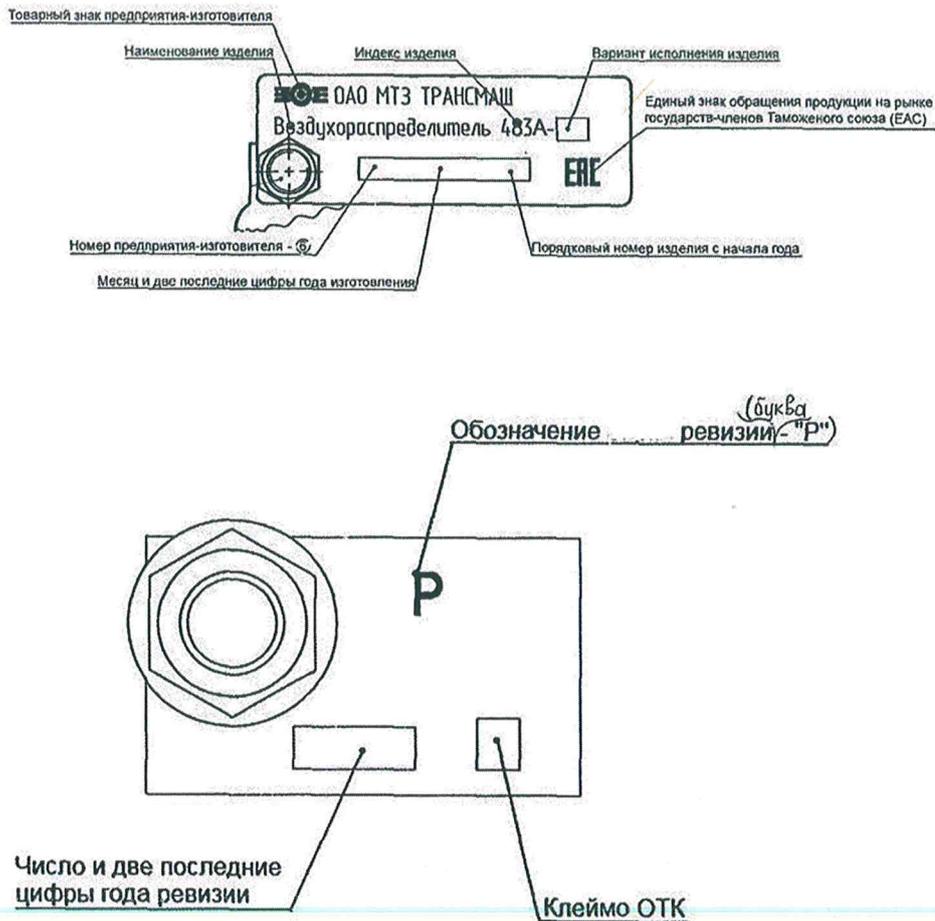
Расположение маркировки на бирке заводской после изготовления и ревизии воздухораспределителя
